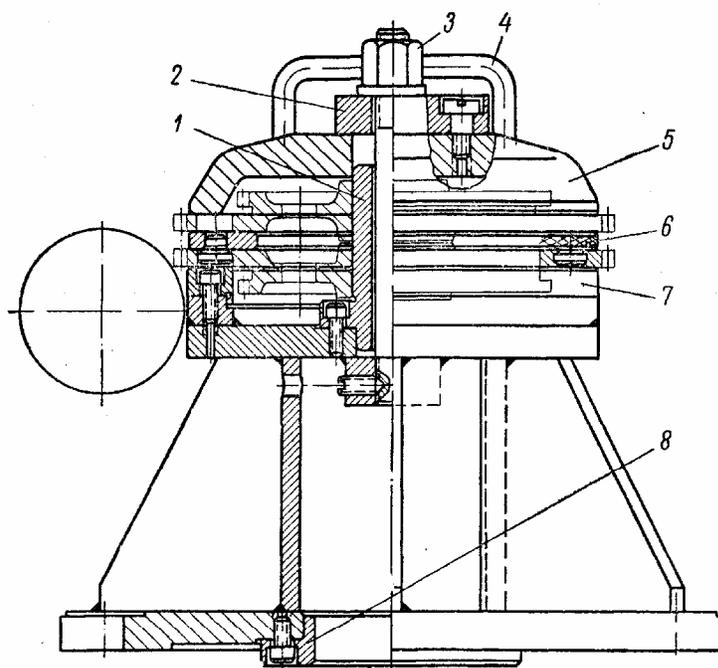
Приспособление для фрезерования зубьев набора двухвенцовых шестерен
